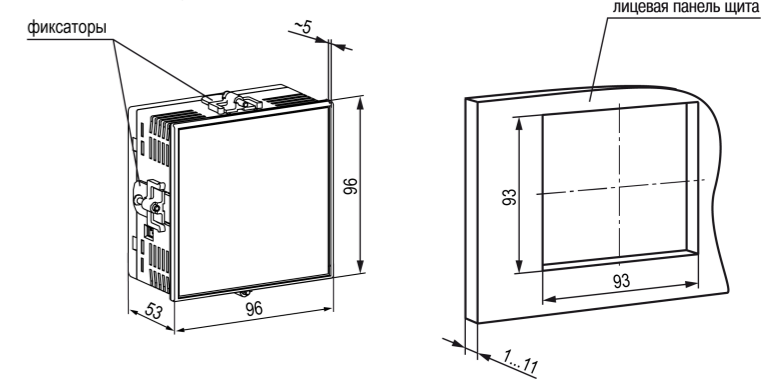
Габаритные размеры корпуса Щ1 и монтажного отверстия в щите
